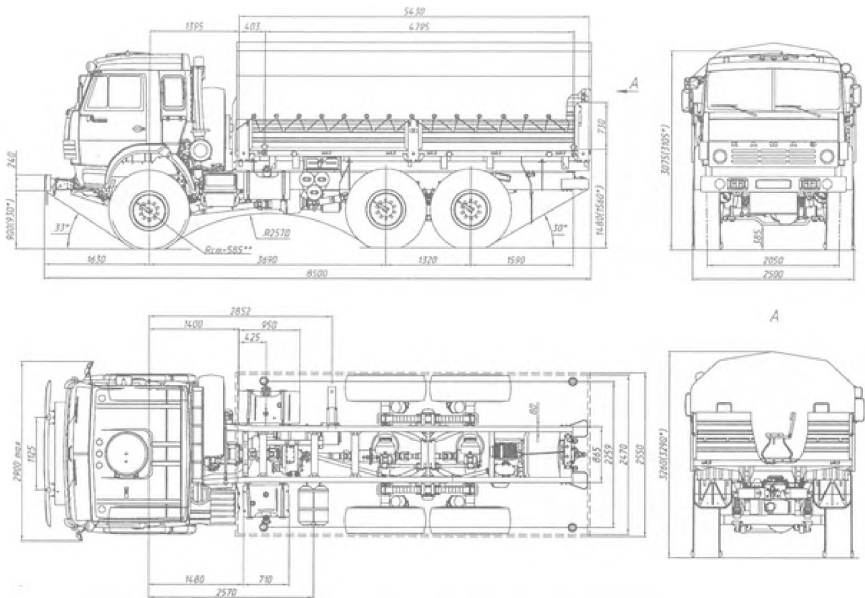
Автомобиль-тягач КАМАЗ-53501. Габаритные размеры.
